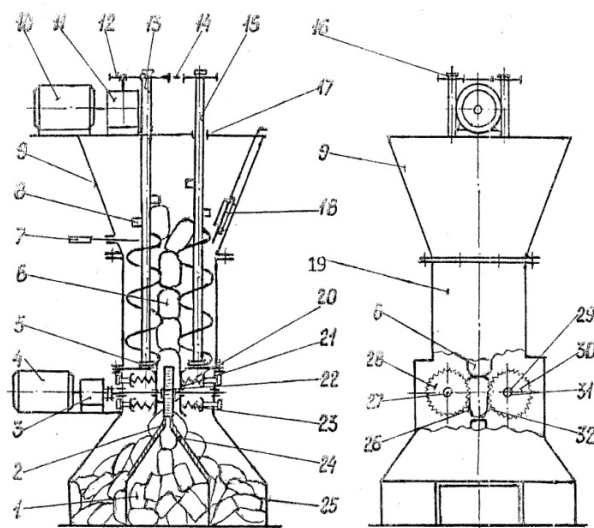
Принципова схема очищення волоських горіхів: 1, 9, 25 – бункери; 2, 24 – розтискачі; 3, 11 – редуктори; 4, 10 – електродвигуни; 5, 17 – вузли опорні; 6 – горіх; 7 – шибер; 8 – ворошилка; 12 – зірочка ведуча; 13, 15, 16 – шнеки; 14 – ланцюгова передача; 18 – датчик наявності горіхів; 19 – корпус; 20, 23 – пружини; 21, 22 – регульовальні колодки; 26, 32 – пази; 27, 31 – вали; 28, 30 – ножі; 29 – різальний механізм.
